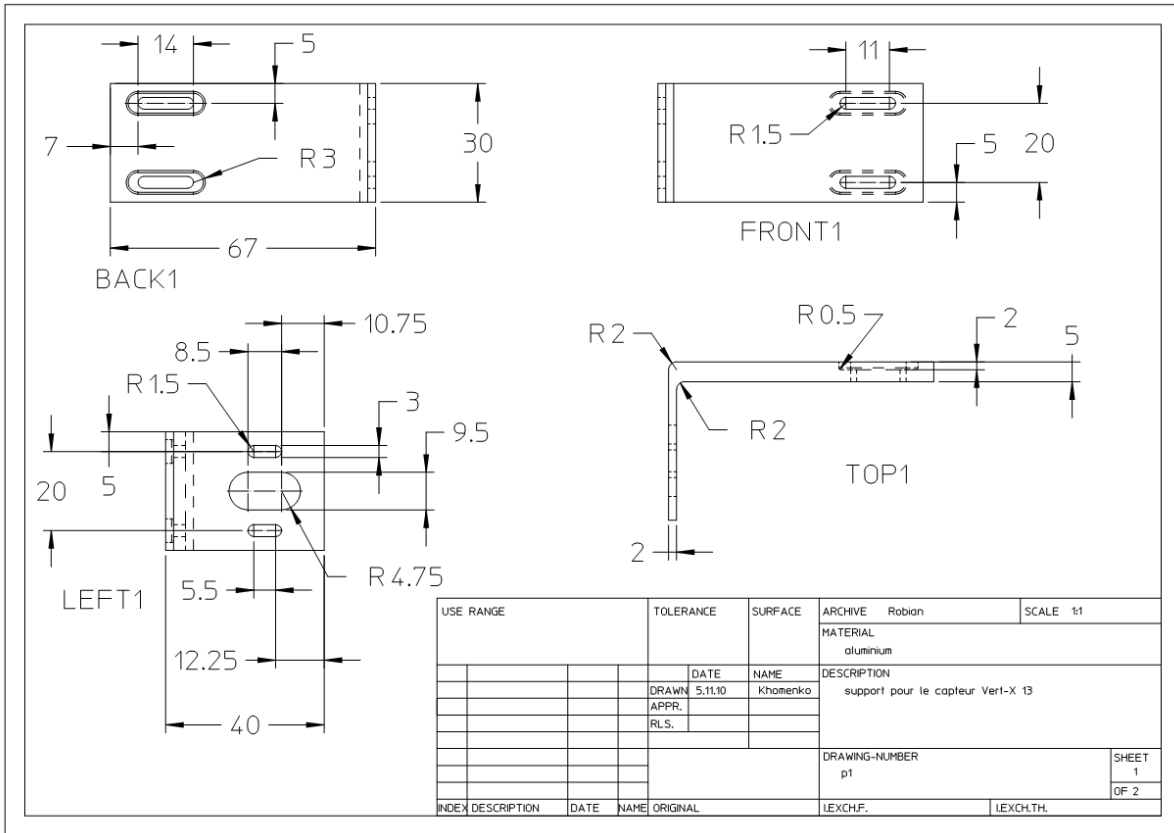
Dessin technique de la pièce réalisée pour supporter le capteur magnétique sans contact
